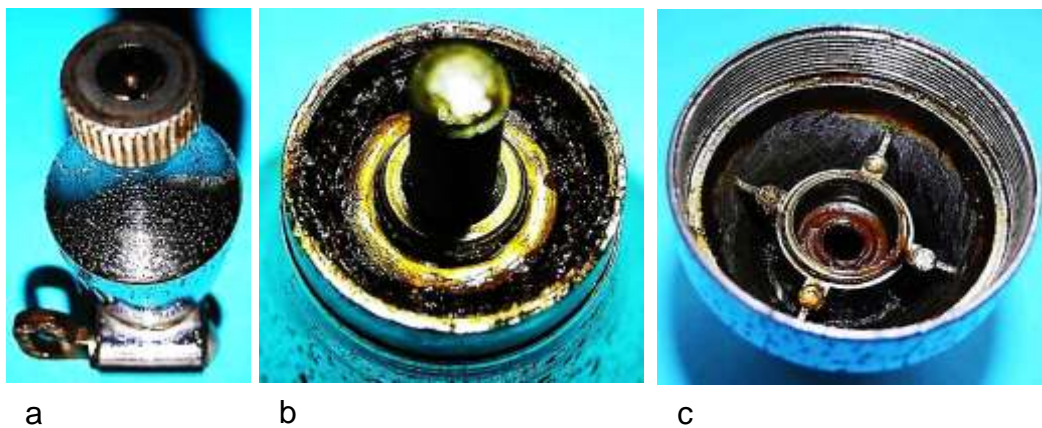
Fliegende Lagerung: a) Reibrad, b) Lager unter dem Reibrad, c) Lagerschale des unteren Kugellagers
